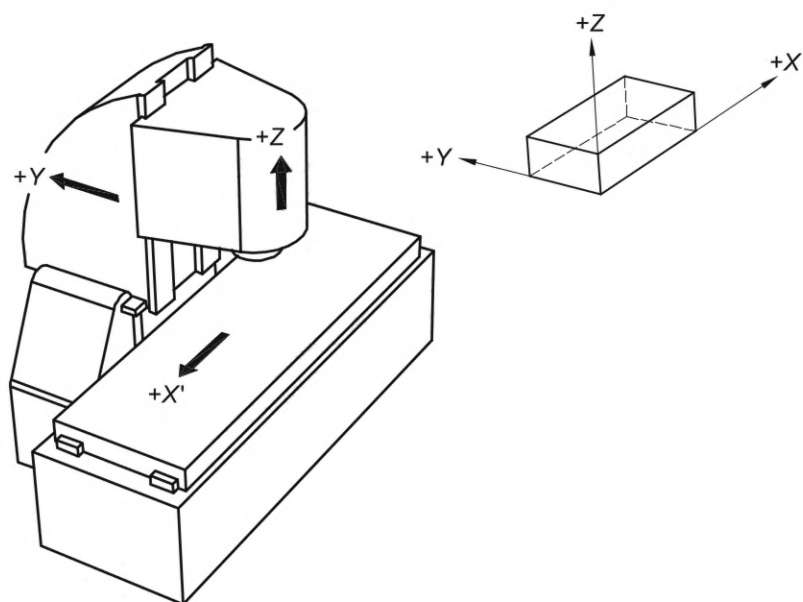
Продольно-фрезерный вертикальный станок
